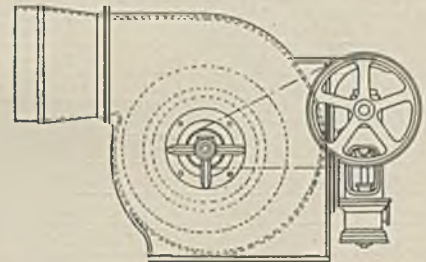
Zentrifugalventilator mit Kolbenmaschine von Dinnendahl.
